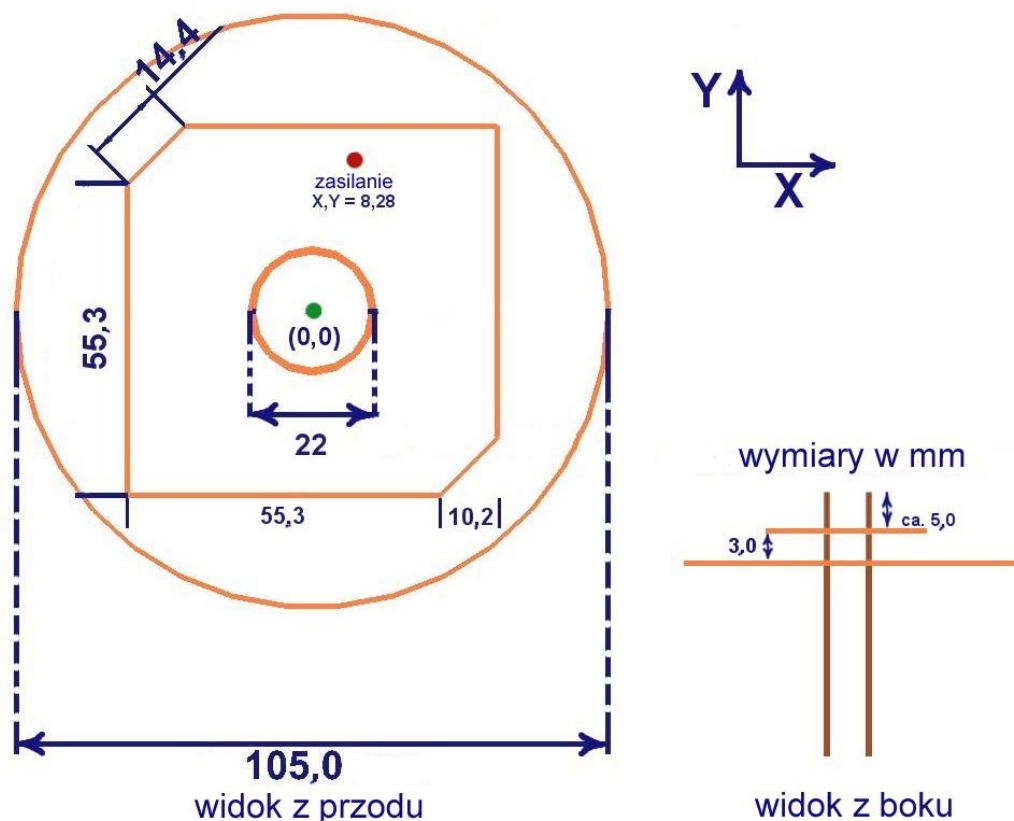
Przykład konstrukcji anteny z rys. 3.4.5
